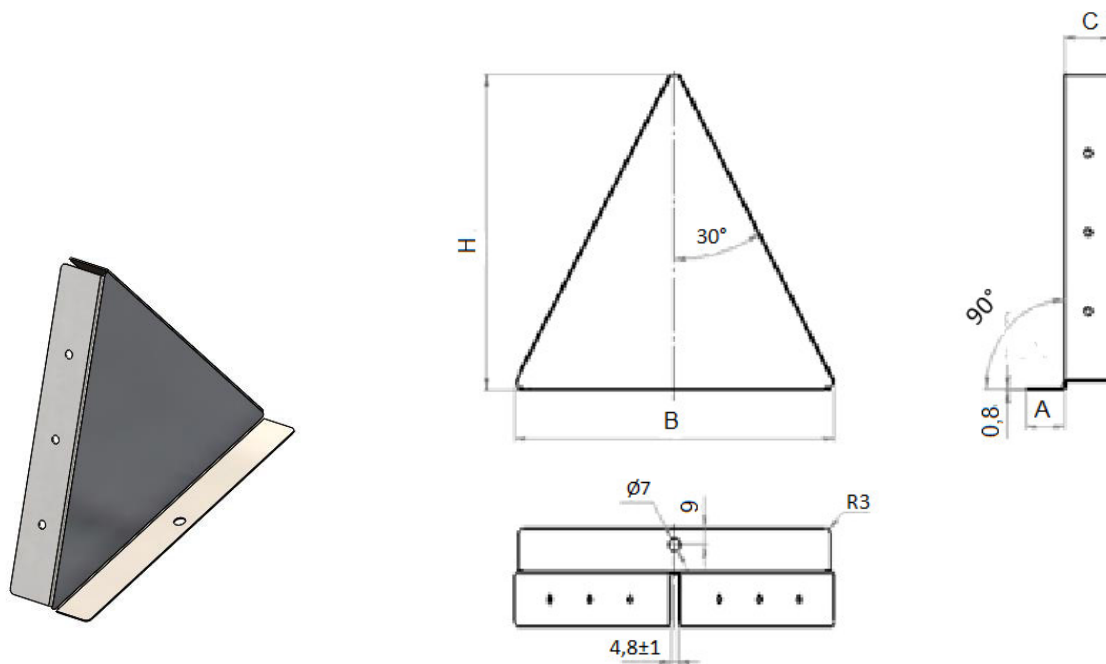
Заглушка для двухскатной крышки, тип SKH20
